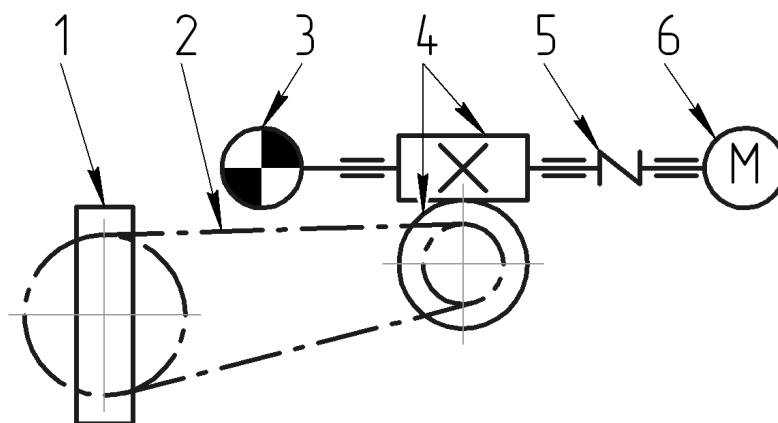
Схема электропривода: 1 – исполнительный орган; 2 – цепная передача; 3 – датчик частоты вращения; 4 – червячный редуктор; 5 – муфта; 6 – электродвигатель.
